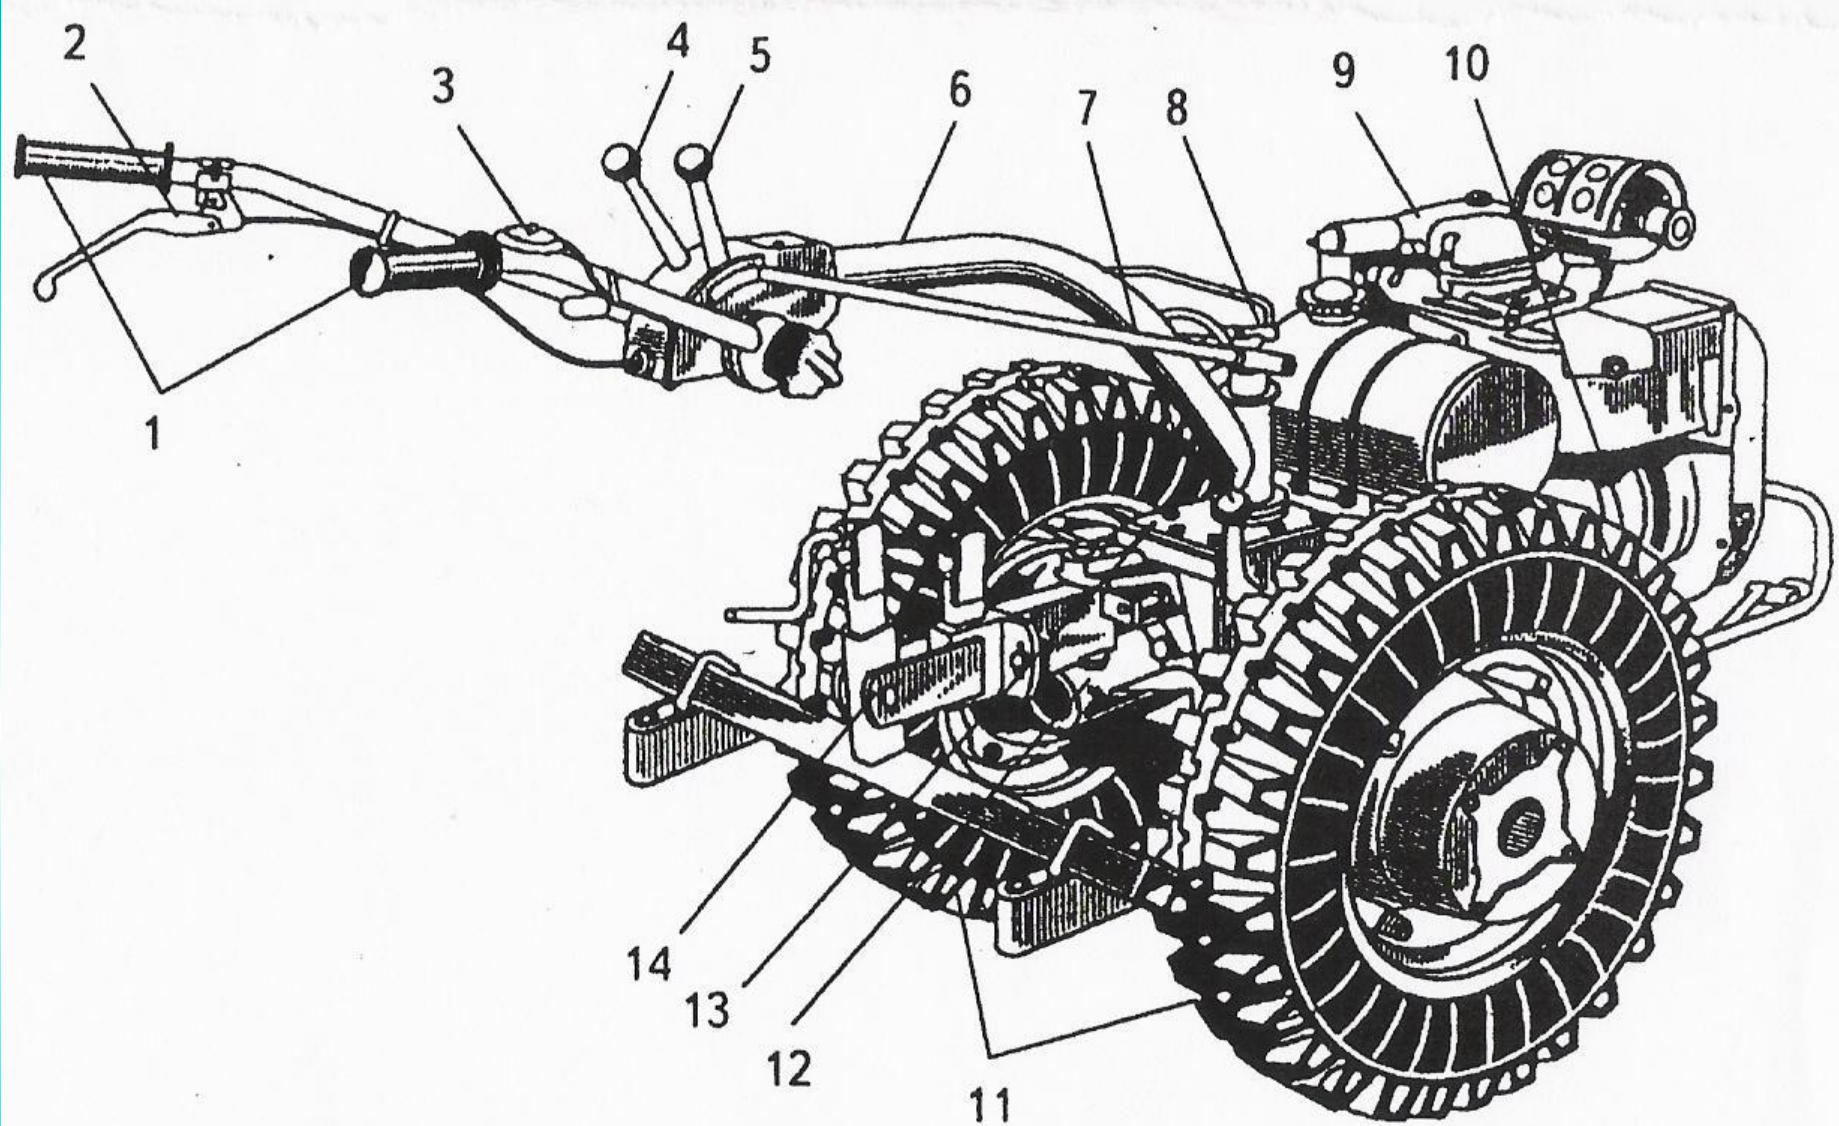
Общий вид мотоблока: 1 – рукоятка управления; 2 – рычаг управления сцеплением; 3 – рычаг газа; 4 – рычаг реверса; 5 – рычаг переключения передач; 6 – рулевая штанга; 7 – рычаг включения ВОМа; 8 – бензобак; 9 – воздушный фильтр; 10 – двигатель; 11 – колеса; 12 – сцепка ВОМа; 13 – стойка; 14 - прицеп
